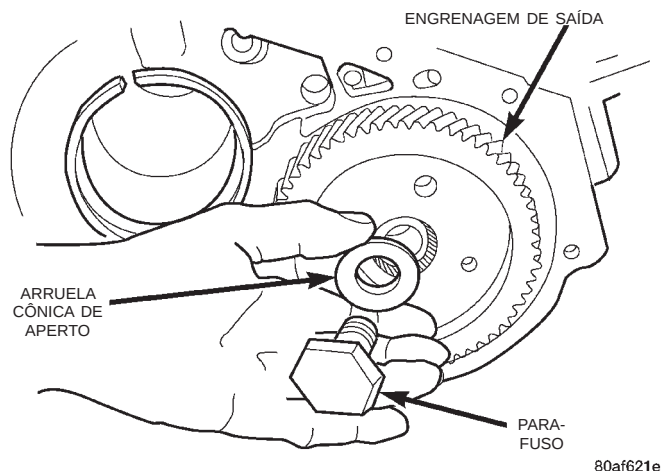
Instalação do Parafuso e Arruela da Engrenagem de Saída
